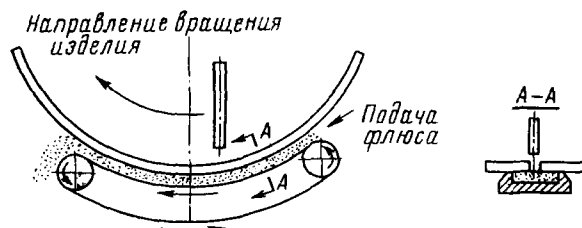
Схема флюсоремной подушки — для сварки кольцевых швов
